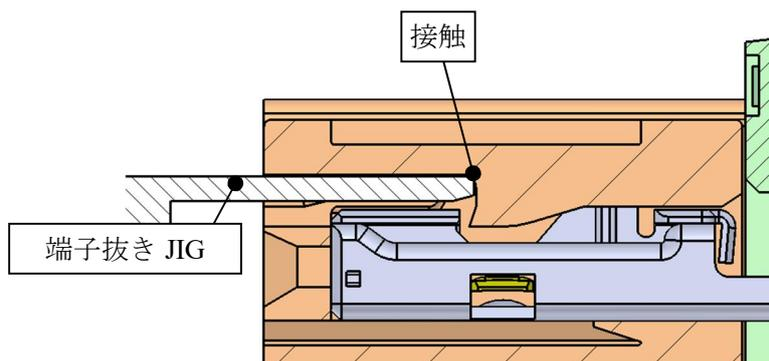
抜き JIG が樹脂ランスに突き当たる位置
